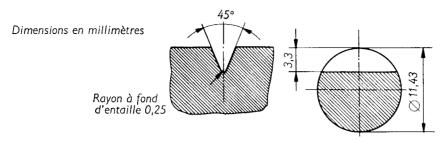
Vue agrandie de l'entaille des éprouvettes à section circulaire
